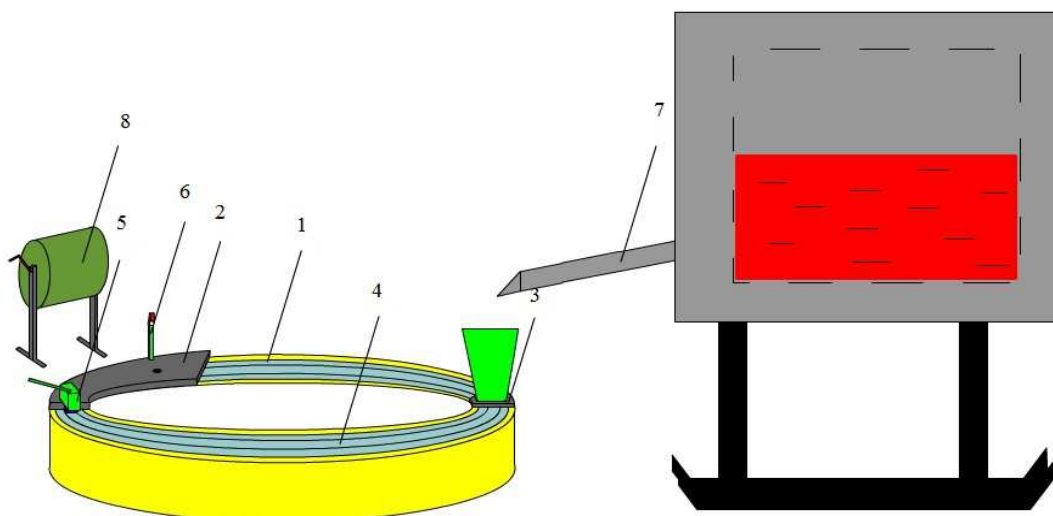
Опытная установка для непрерывного прессования способом «Конформ».
